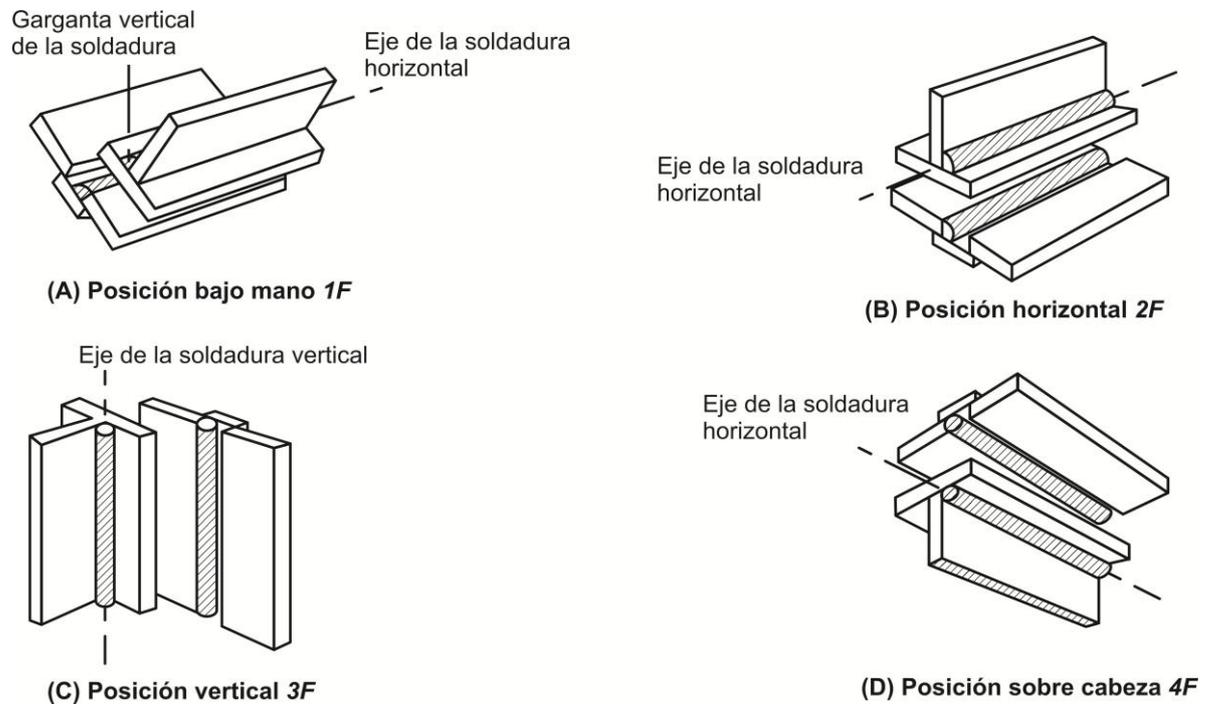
Posiciones de ensayo de chapa para soldaduras de filete.
